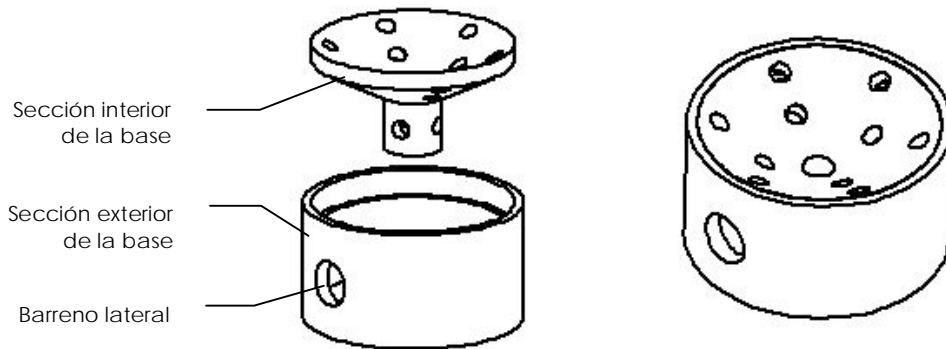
Vista explosiva y ensamble de la base del cojinete neumático
